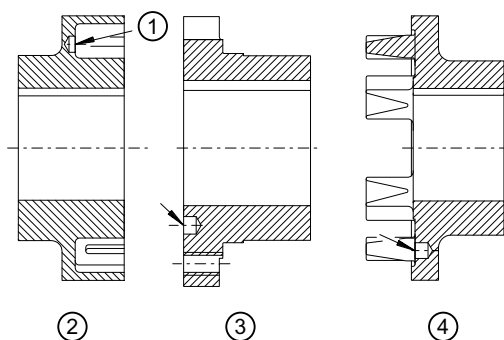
Position du trou d'équilibrage pour l'équilibrage à un plan
